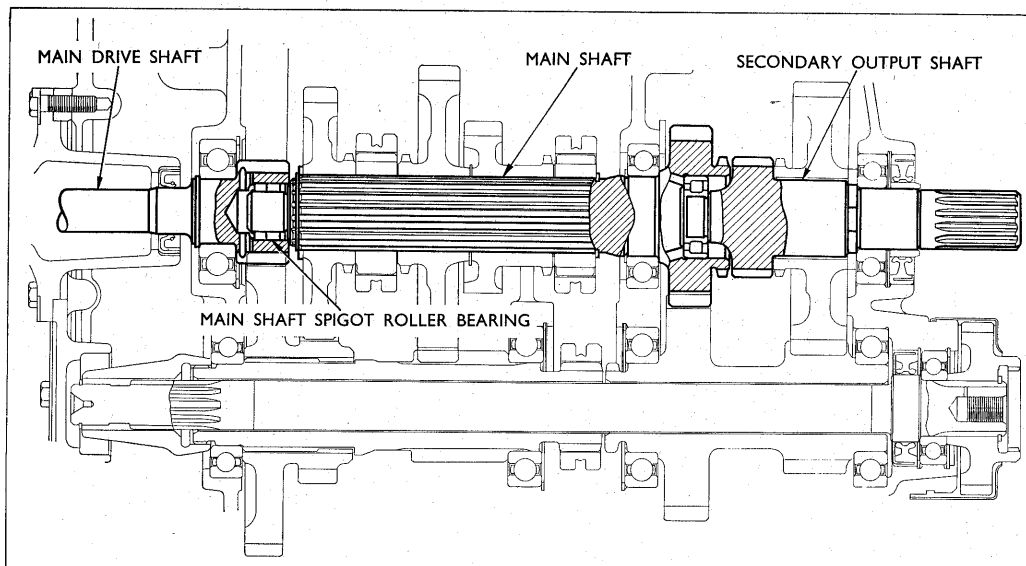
De fuldt optrukne dele er specielle for Super Dexta.
